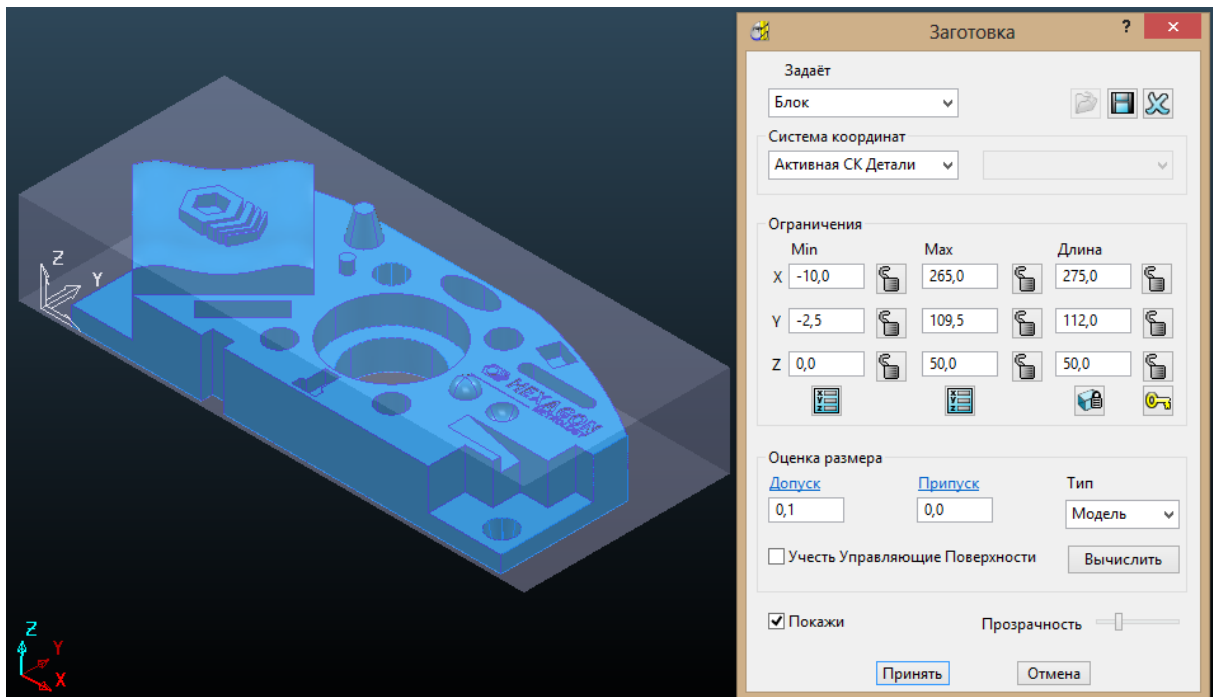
Створення заготовки в середовищі «PowerMILL».
